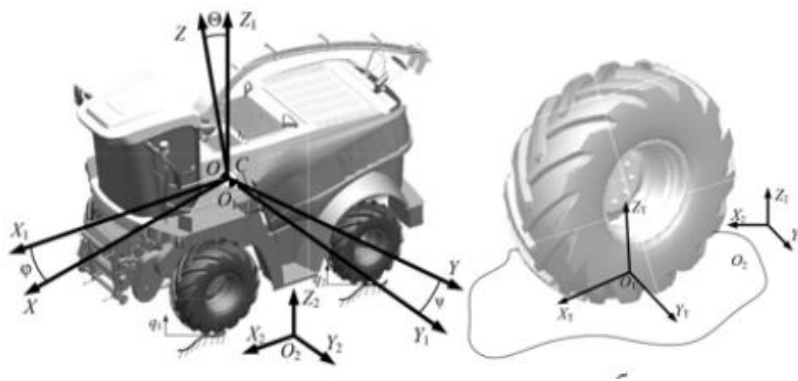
Положення прийнятих систем координат для корпусу (а) та коліс (б)
